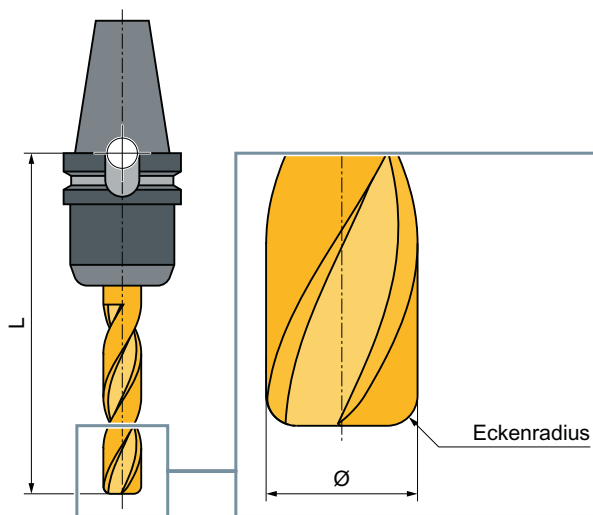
3D-Werkzeug am Beispiel eines Schaftfrers mit Eckenverrundung (Typ 121)
